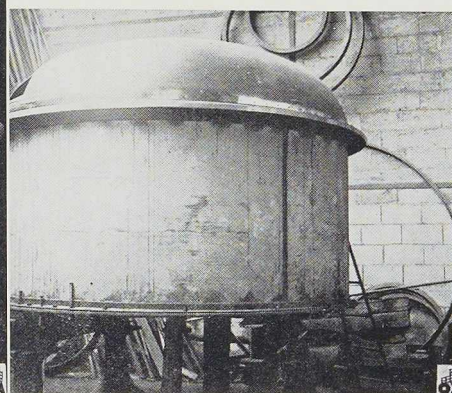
Ventilateur en acier inoxydable soudé à l'arc.
